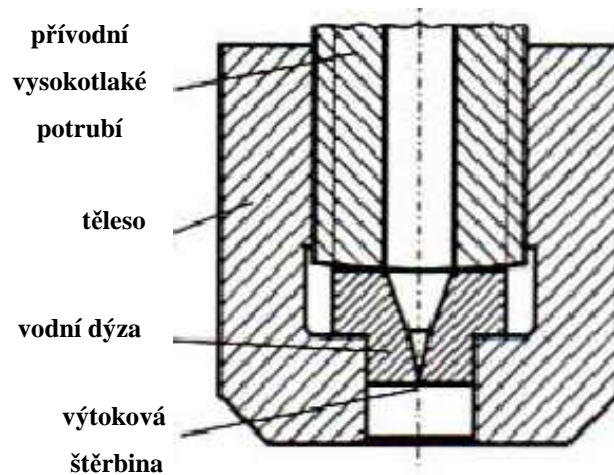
Hlavní komponenty zařízení pro obrábění vodním paprskem. [1]
